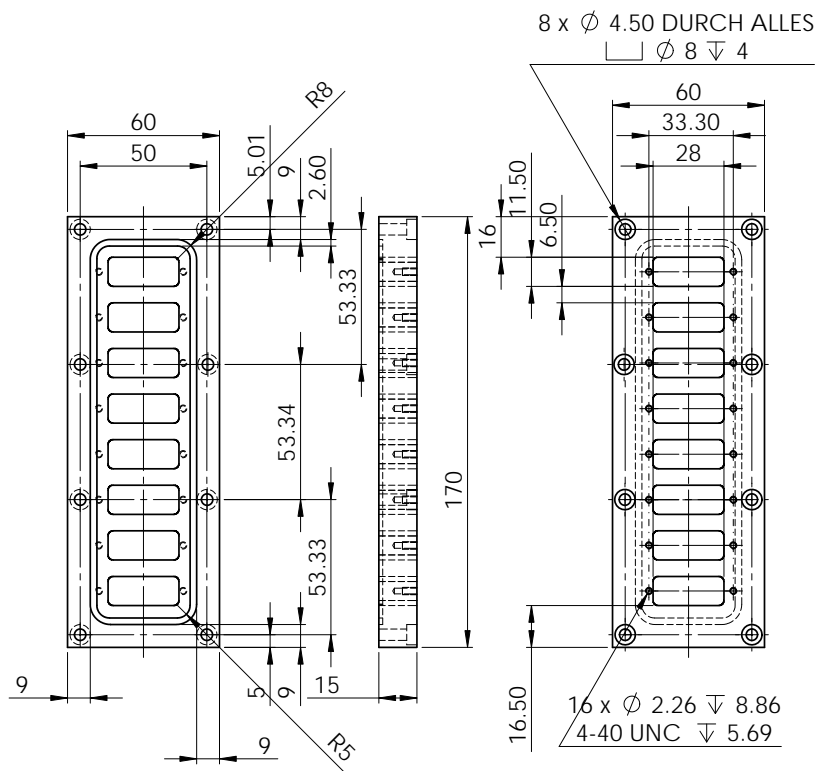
Technische Zeichnung des Steckerflanschs.
